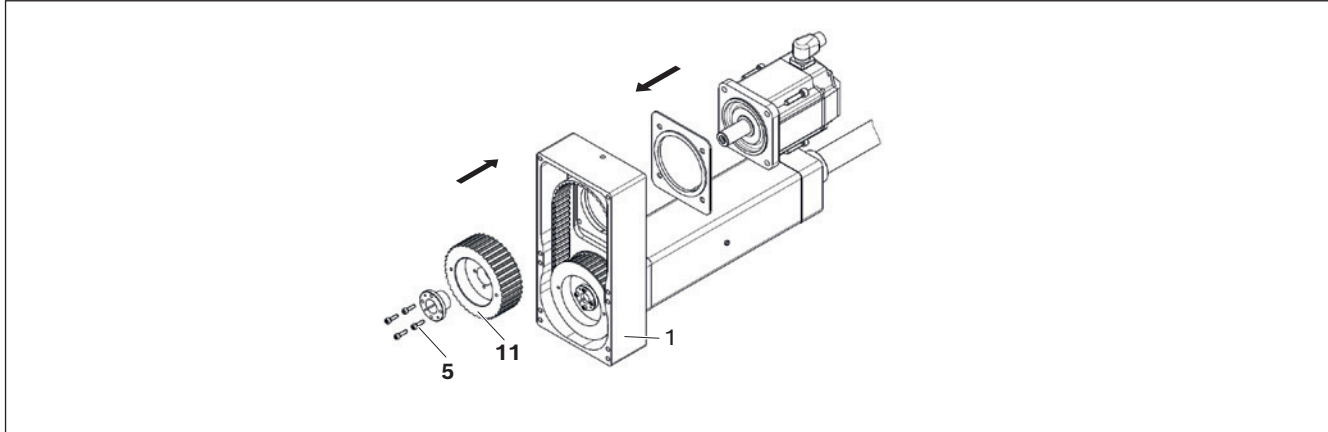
Motor und motorseitiges Riemenrad montieren, $i = 1$
